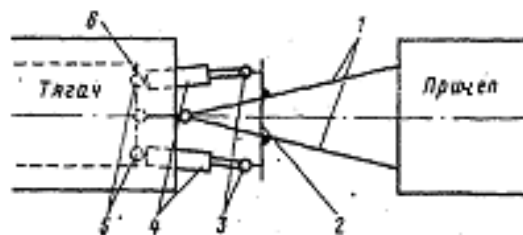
Схема стабілізатора фірми «Гірлінг»
